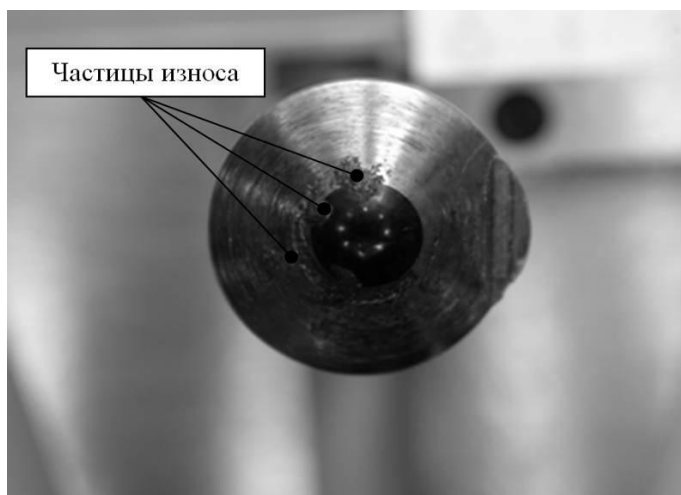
Рабочая поверхность инструмента загрязненная абразивными и инородными частицами износа
